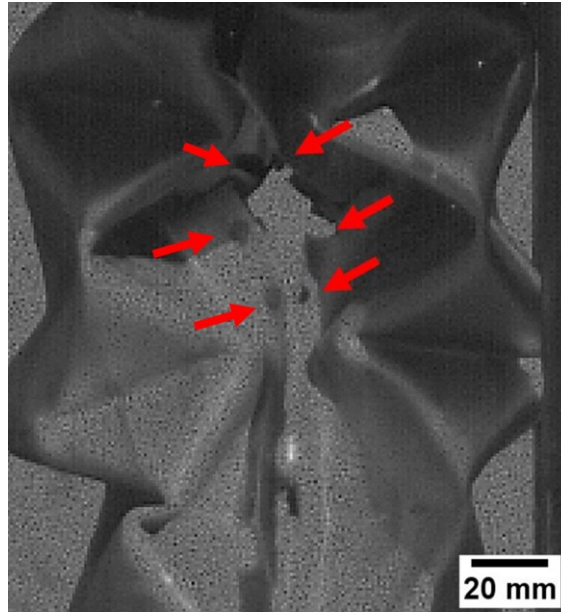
Falha dos pontos de solda RSW durante teste de compressão do crash box “Origami RSW 4”. (Próprio Autor)
